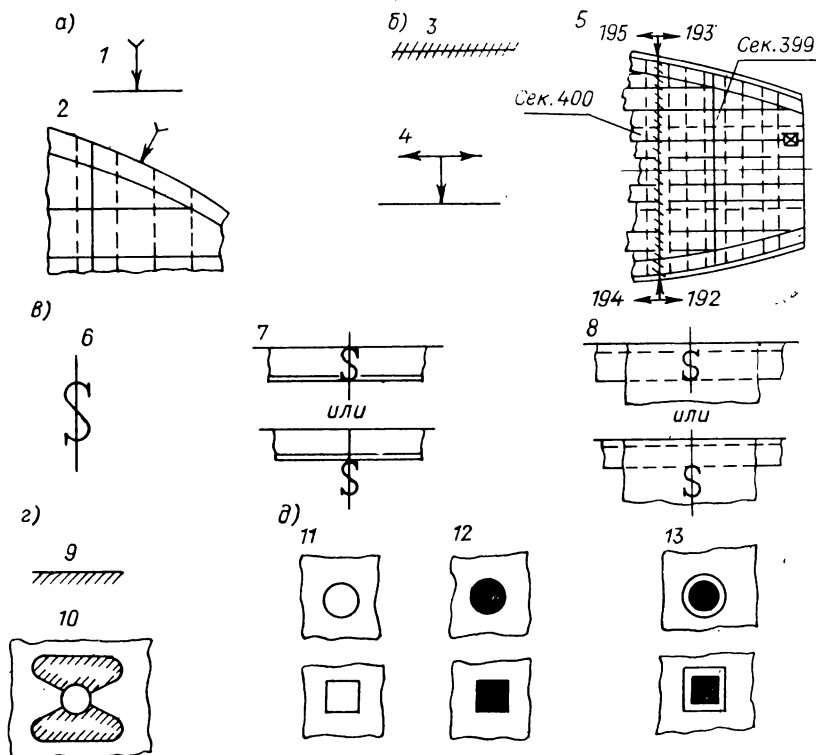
Условные графические обозначения на чертежах корпусных конструкций:
